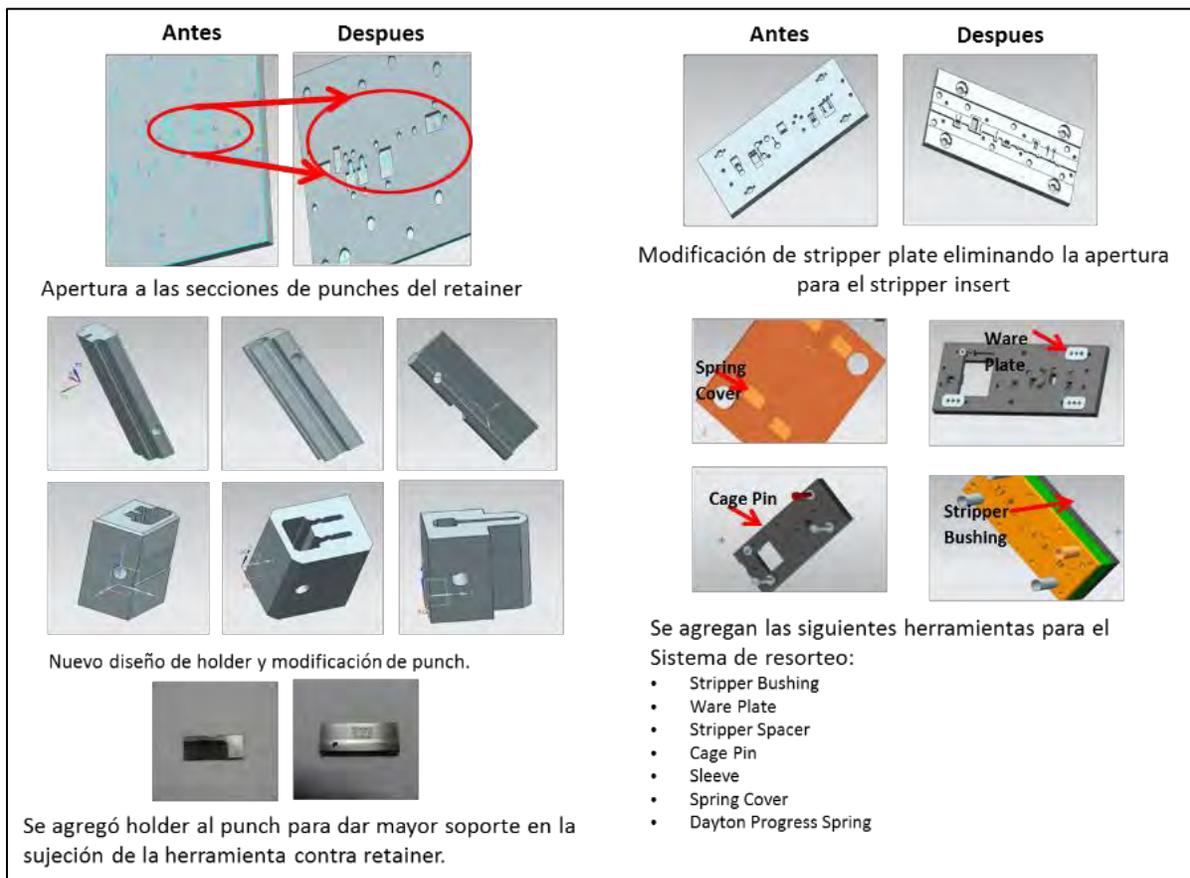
Rediseño de herramientas del troquel 13833340 MA1
